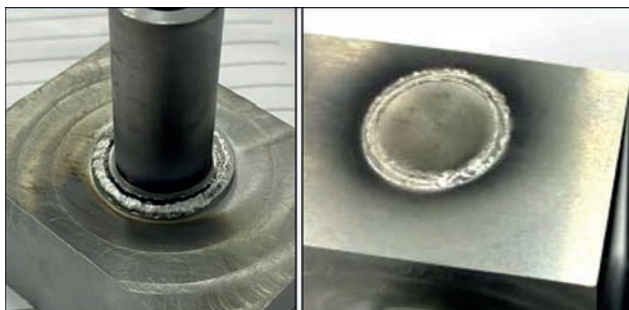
Формування кільцевих швів з відбортуванням кромки, що імітують з'єднання ніпель-корпус та пробка-корпус клапана
